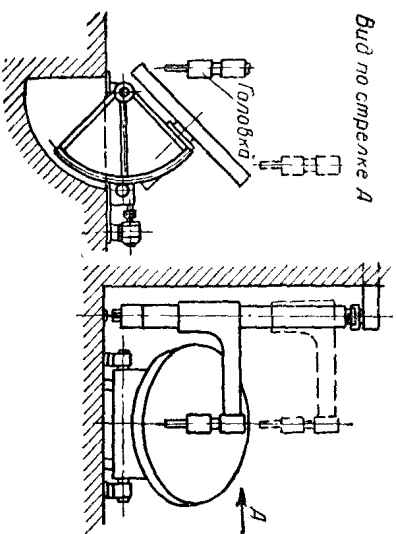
Схема установки для сварки круговых швов.
